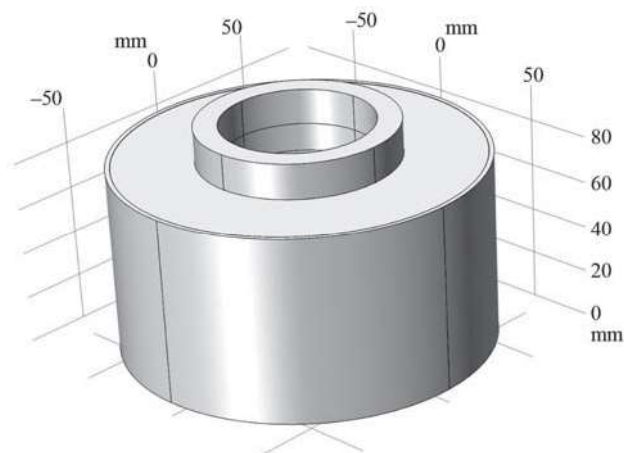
Эскиз готового изделия при помощи встроенного модуля CAD
